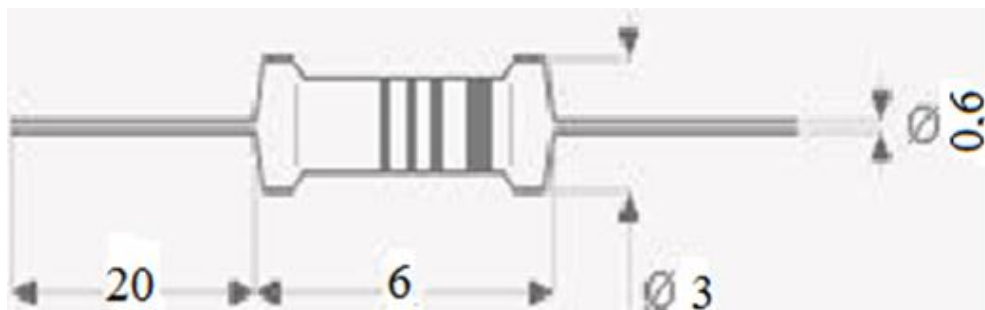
Габаритні розміри резистора C2-33H
